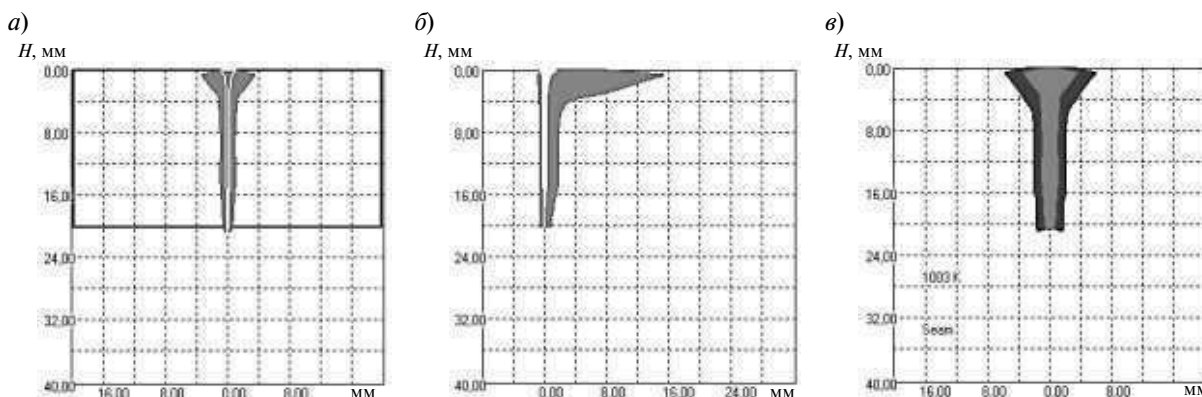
Лазерно-дуговая сварка в верхнем пространственном положении: *a* — зона проплавления; *б* — сварочная ванна (продольный вид); *в* — сварное соединение
